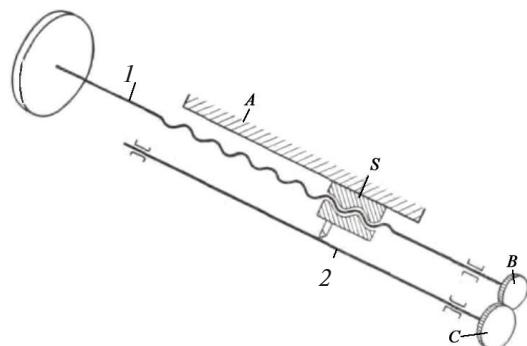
Схема токарно-винторезного станка Нартова с механизированным суппортом
